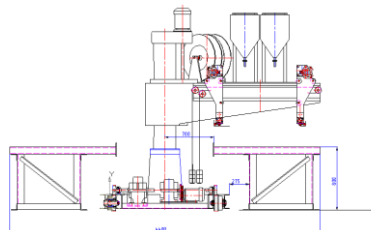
Зовнішній вигляд верстата для зварювання двутаврів
